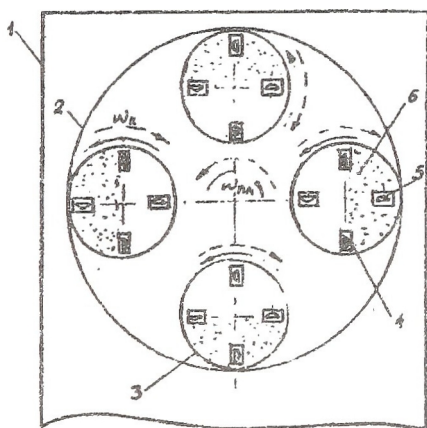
Схема установки и закрепления лопаток компрессора в контейнере УПДК при  $\alpha=90^\circ$  (→ направление потоков рабочей среды): 1-корпус; 2-планшайба; 3-контейнер; 4-узел захвата; 5-лопатка; 6-рабочая смесь
